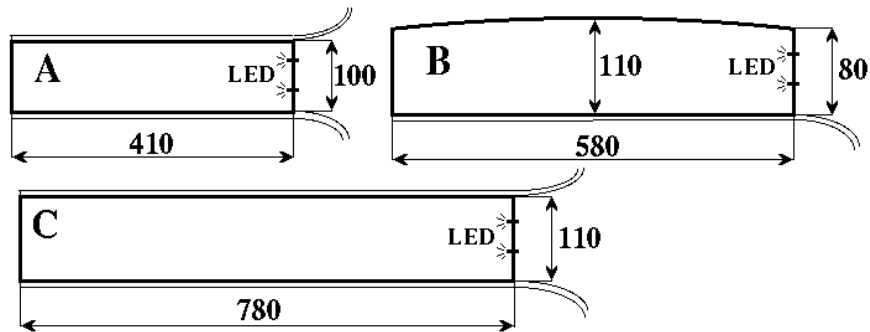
Forme et dimensions des compteurs à 40°
